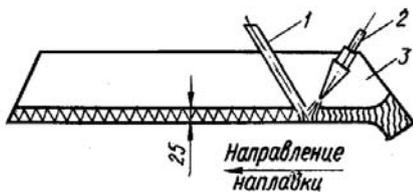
Схема наплавки лезвия лемеха твердым сплавом с помощью газовой горелки: 1 — пруток твердого металла; 2 — горелка; 3 — лемех
